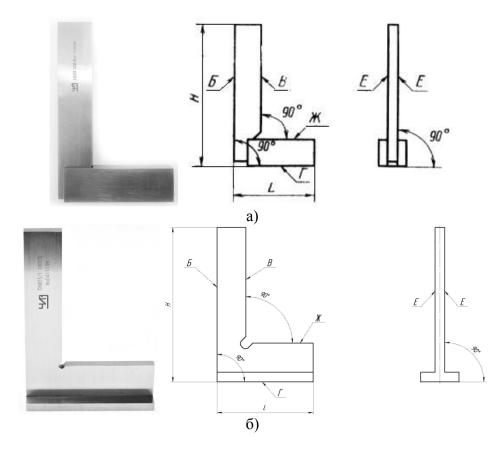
Общий вид угольников УП, обозначение основных размеров и поверхностей
